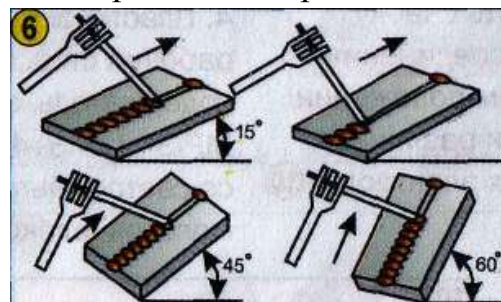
Сварка стыковых соединений в наклонном положении.
